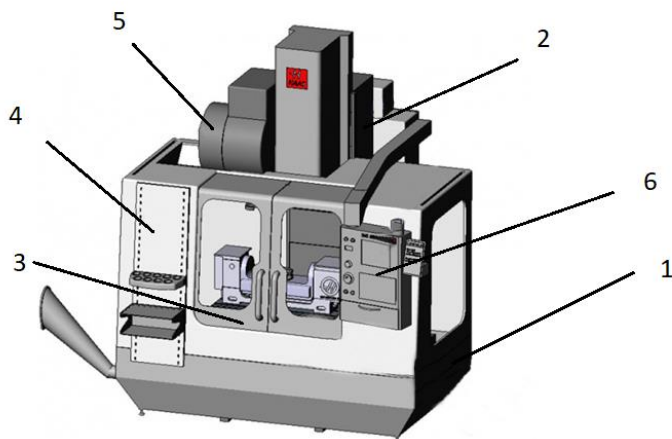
Вертикальний фрезерний верстат з ЧПУ:
